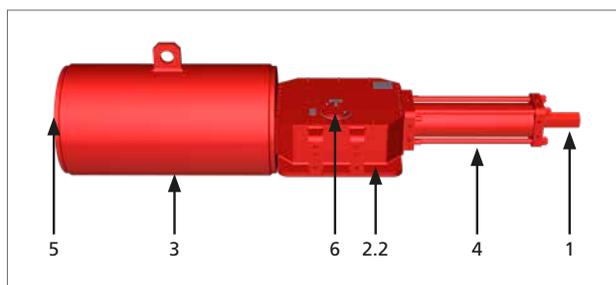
Componenti principali GH/S (Corpo saldato)
